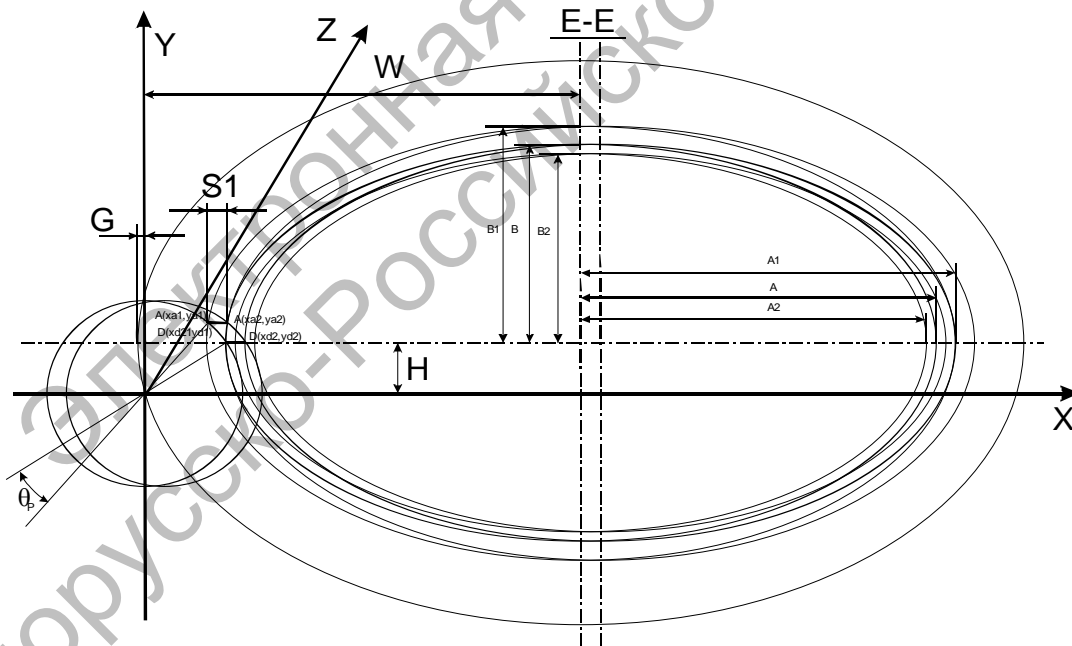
Система координат и схема определения параметров среза и площадки контакта резца с заготовкой по передней поверхности режущего элемента
